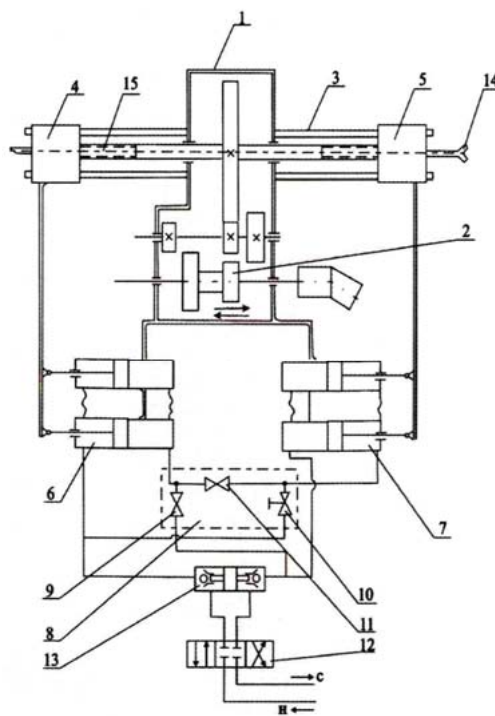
Внешний вид и кинематическая схема бурового станка СБР—400
